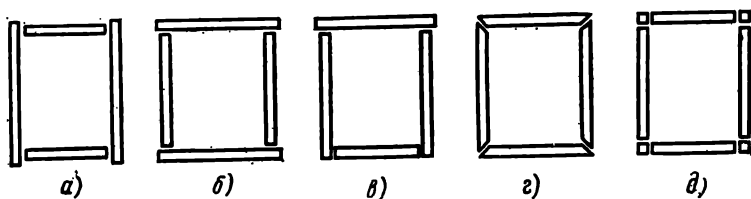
Схемы типовых расположений стенок корпусной мебели: а — с вертикальными проходными стенками, б — с горизонтальными проходными стенками, в — с комбинированным расположением стенок, г — с усовым расположением стенок, д — с угловым вкладным соединительным элементом
